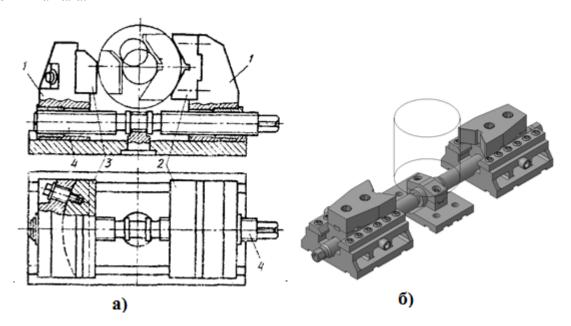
Универсальные самоцентрирующие тиски с двумя постоянными подвижными губками
